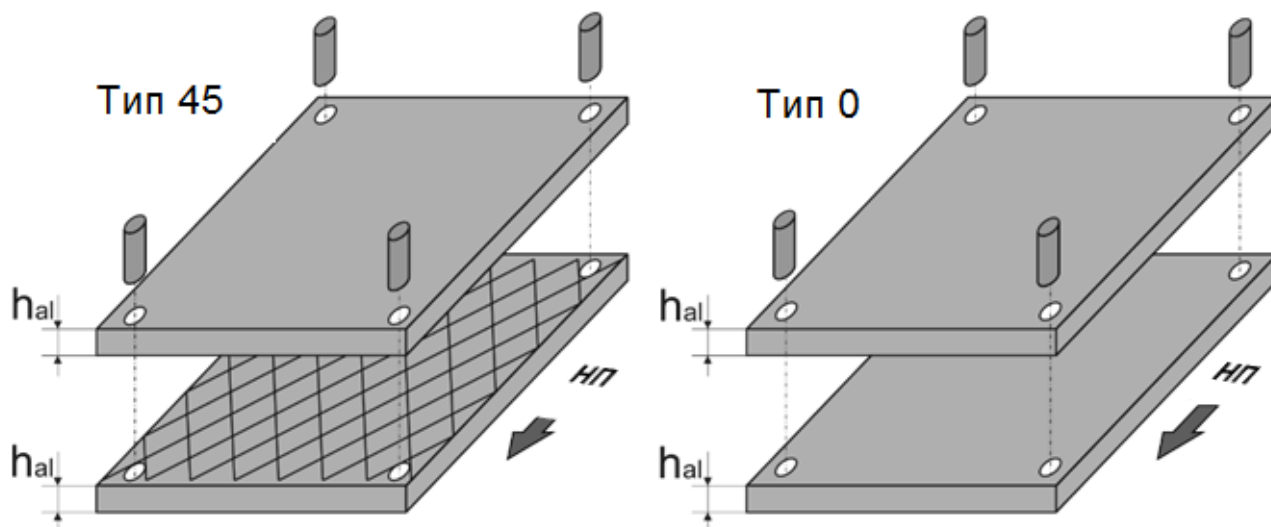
Схема підготовки заготовок прокатки армованих композитів:
